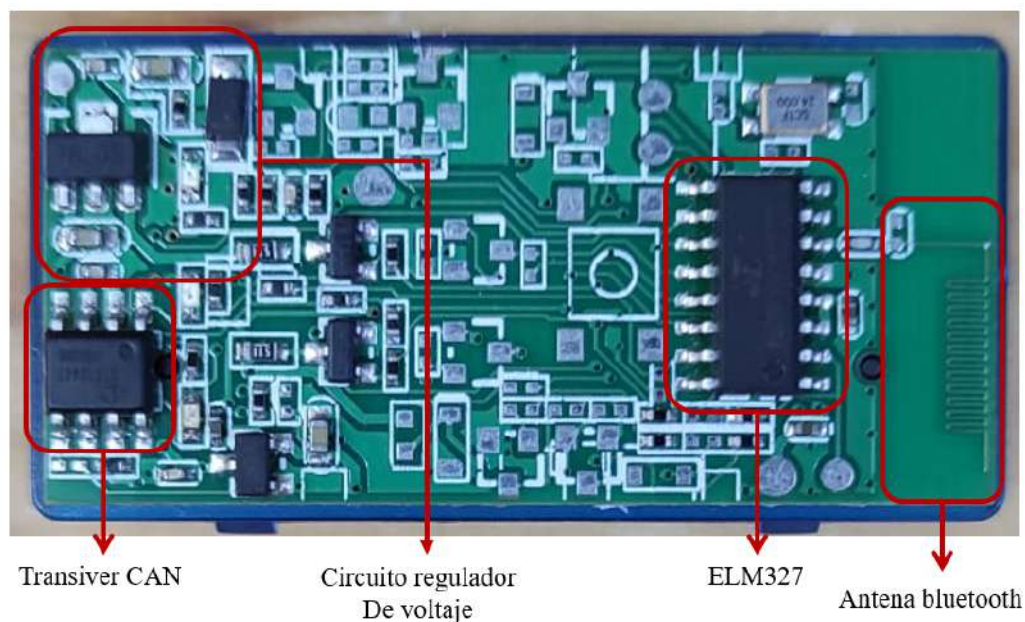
PCB del módulo OBDII ELM327 [18]
